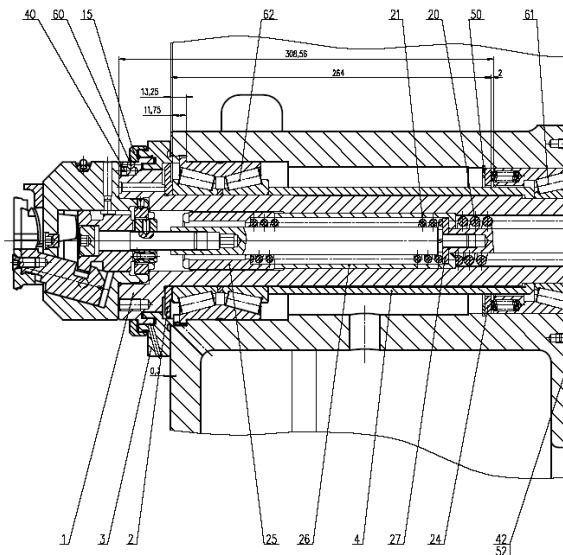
Конструктивная схема шпиндельного узла станка ТАК-103
